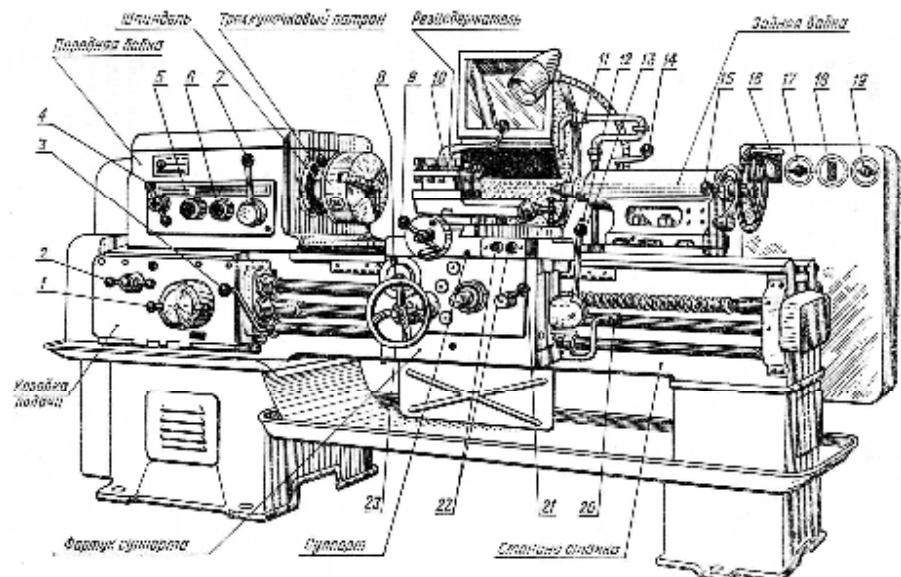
Общий вид токарно-винторезного станка 1К62.
